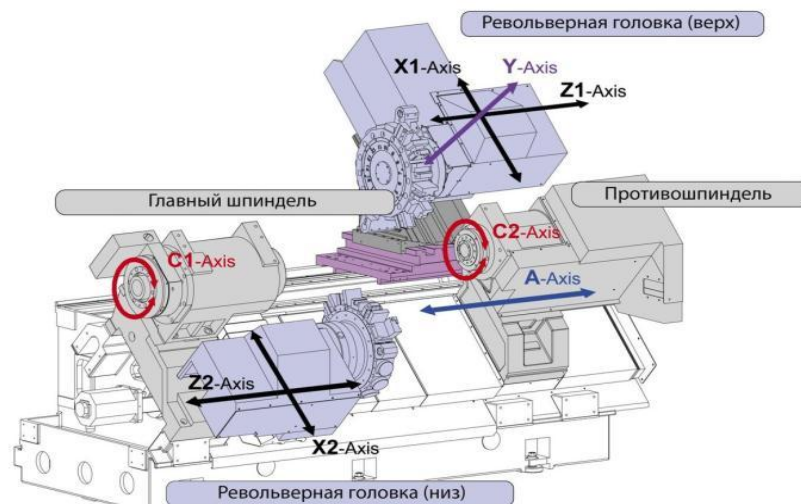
Конструкция обрабатывающего центра CTX gamma 2000
